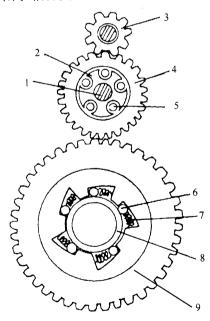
减速装置 1-中间铀;2-尼龙骨架;3-小齿轮;4-中间齿轮;5-滚柱轴承;6-滚柱;7-弹簧;8-传动导
